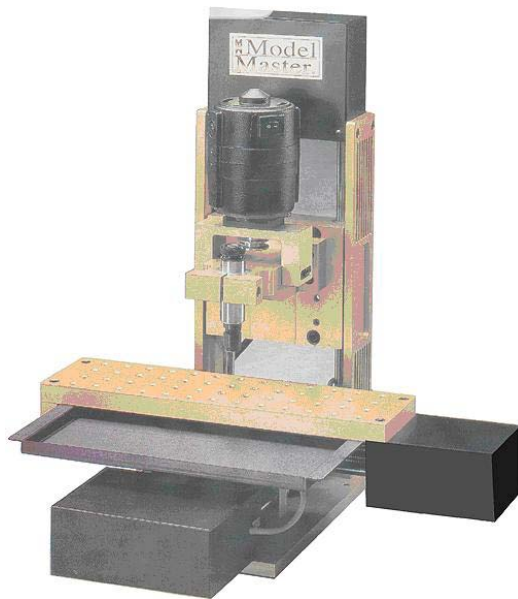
Equipamento para usinagem convencional CNC, Model Master.
